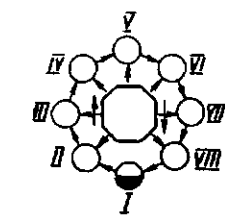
Наладка восьмишпиндельного полуавтомата для одноциклового обработки корпусной детали с применением телескопических суппортов
